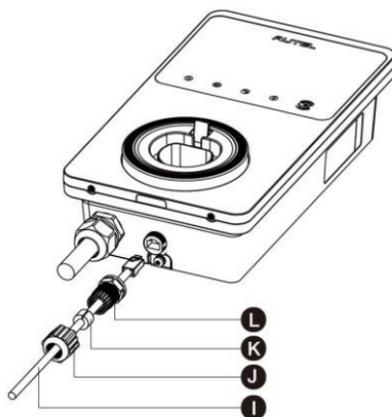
Collegamento del pressacavo Ethernet waterproof
